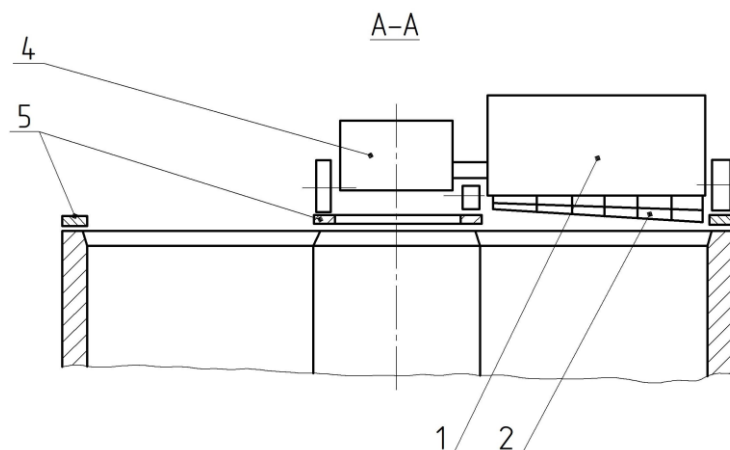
Вид сбоку (сеч. А - А рис. 46) на пресс-форму и устройство для укладки абразивной смеси
